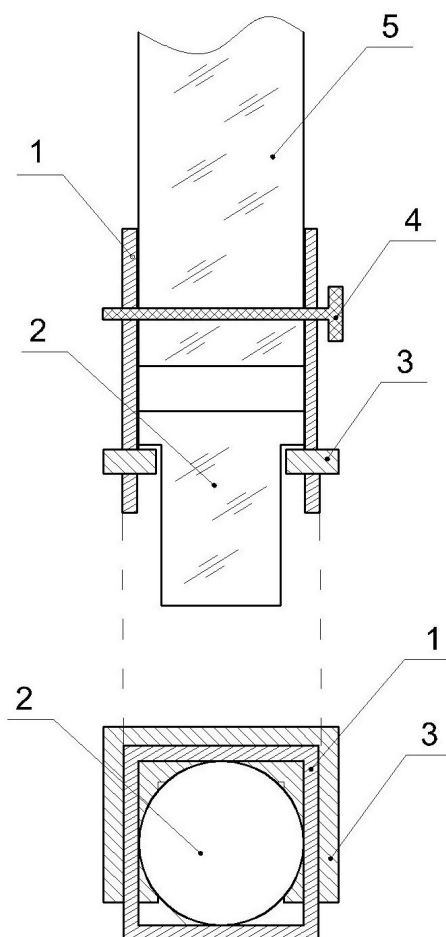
Схема кріплення затравки до штока: 1- ячейка затравкоутримувач (Pt); 2- затравка; 3- фіксатор затравки (Pt); 4- сапфіровий штифт; 5- шток механізму витягування/обертання.
